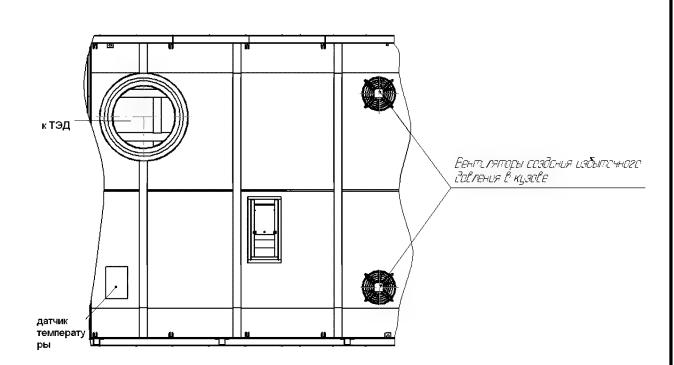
Форкамера вентиляторов избыточного давления вид из машинного отделения.
